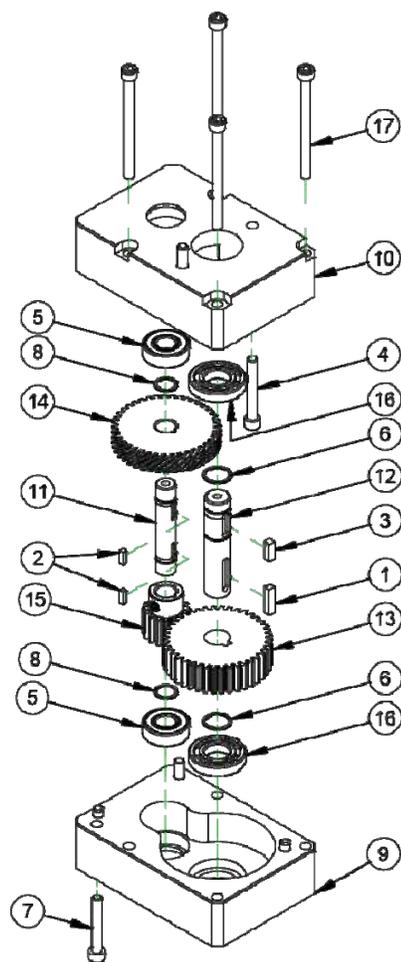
Узел фрезерной головки, HSK 40, пневматика, прямоугол. 68455
